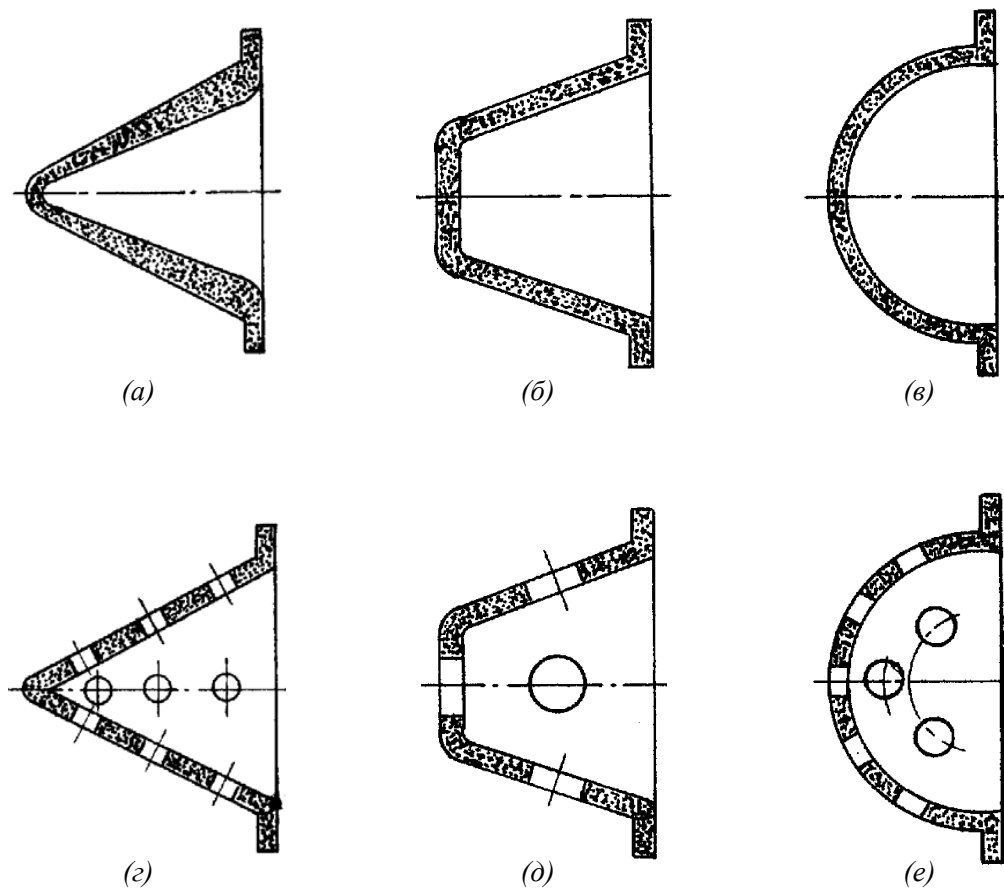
Различные варианты конструктивного исполнения диафрагмы (а–е) газосборного ресивера из пористой звукопоглощающей газопродуваемой структуры типа прессованного сетчатого материала (ПСМ), металлорезины (МР)
